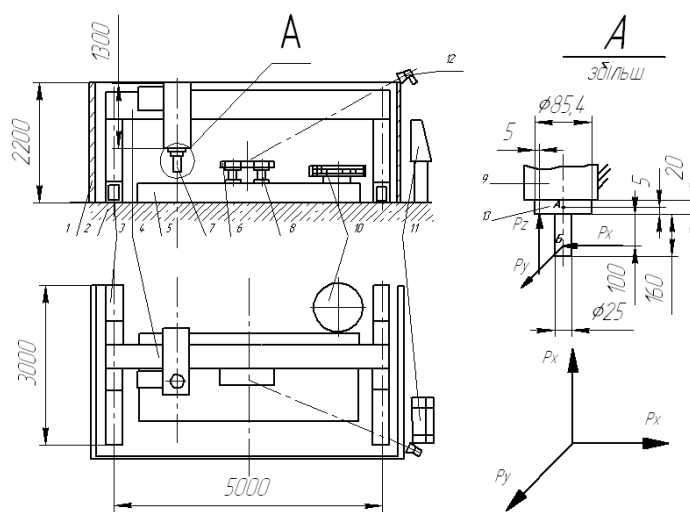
Технологічна схема верстата «Energia» (Італія): 1 – огорожа; 2 – фундамент; 3 – напрямна; 4 – міст верстата; 5 – стіл; 6 – виріб; 7 – робочий інструмент; 8 – вакуумне фіксує пристосування; 9 – шпindelний вузол; 10 – інструментальний барабан; 11 – пульт керування; 12 – стробоскопічний тахометр.
